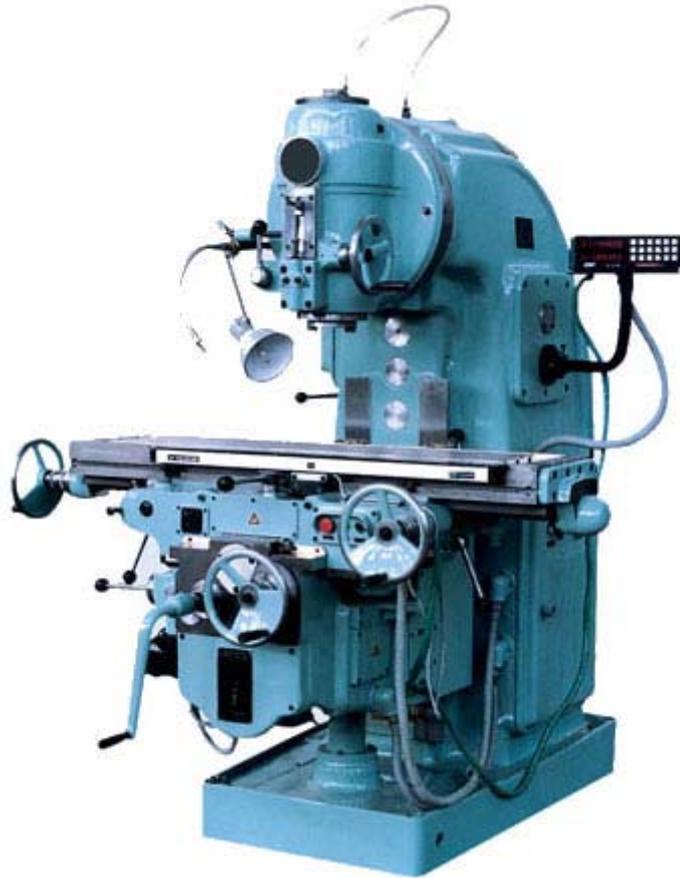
Вертикально-фрезерный консольный верстат 6P12
